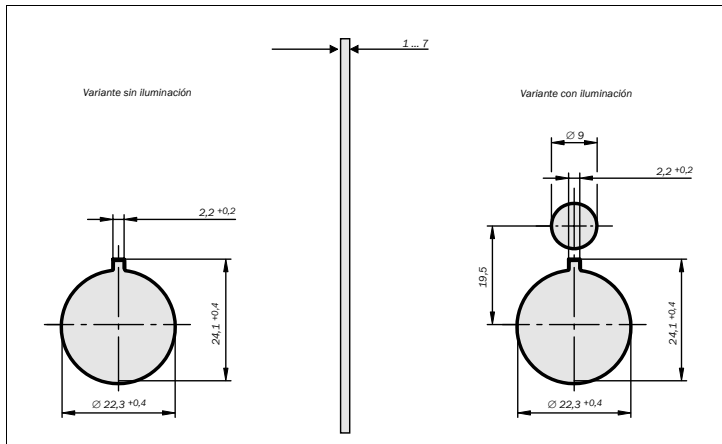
Croquis de dimensiones de los orificios de montaje para la versión de montaje en panel (mm)
